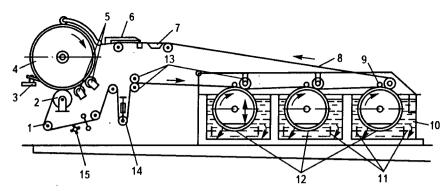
Схемы работы листоформовочной машины: 1 – направляющий валик; 2 – опорный валик; 3 – срезчик; 4 – форматный барабан; 5 – пресс-валы; 6 – регулировочный валик; 7 – вакуум-коробка; 8 – сукно; 9 – отжимной валик; 10 – ванна; 11 – мешалка; 12 – сетчатый цилиндр; 13 – отжимные валки; 13 – натяжной валик: 14 – отбойный валик
